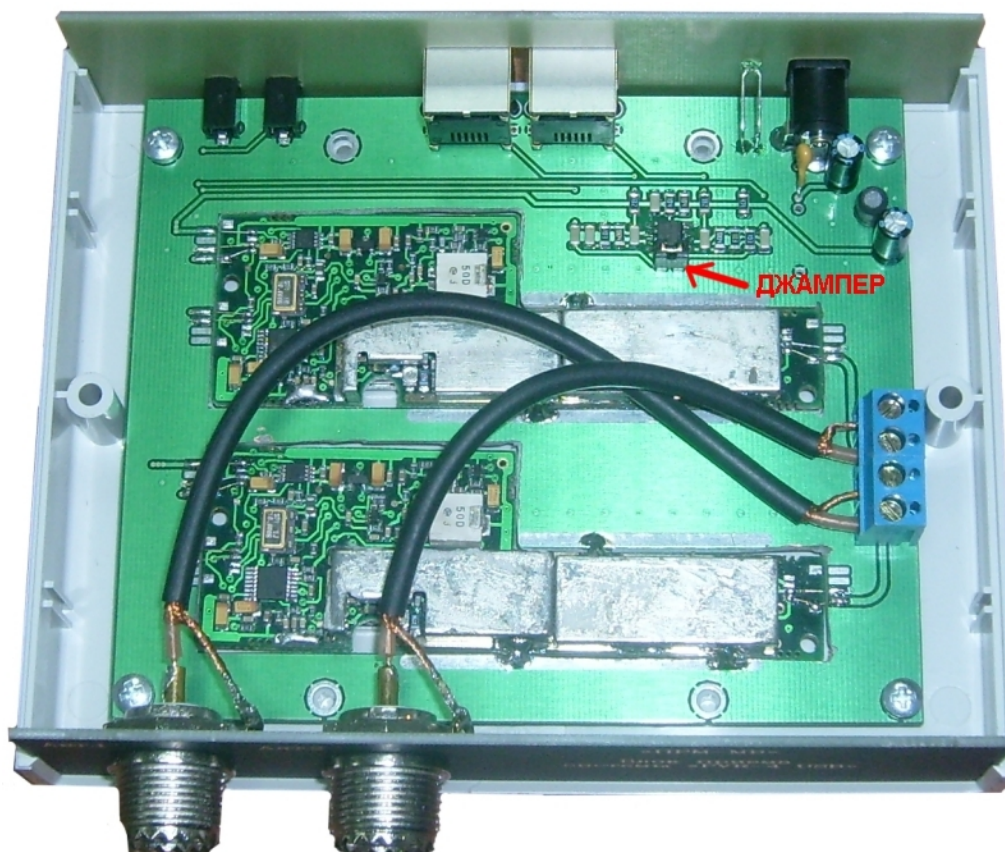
Вид блока ПРМ-МВ.02 с открытой крышкой
